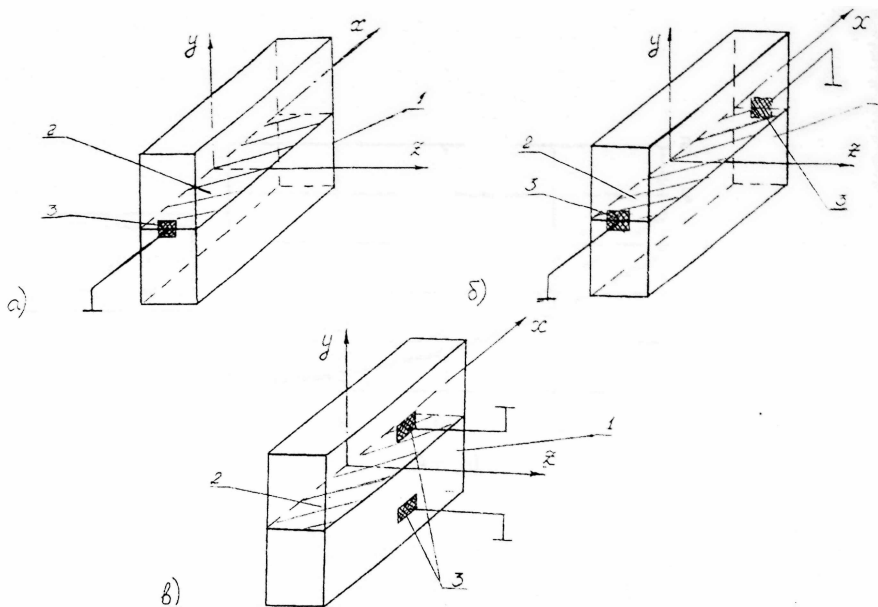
Схемы расположения заземлений при сварке: 1 - свариваемые образцы; 2- плоскость стыка; 3 - места заземлений.
